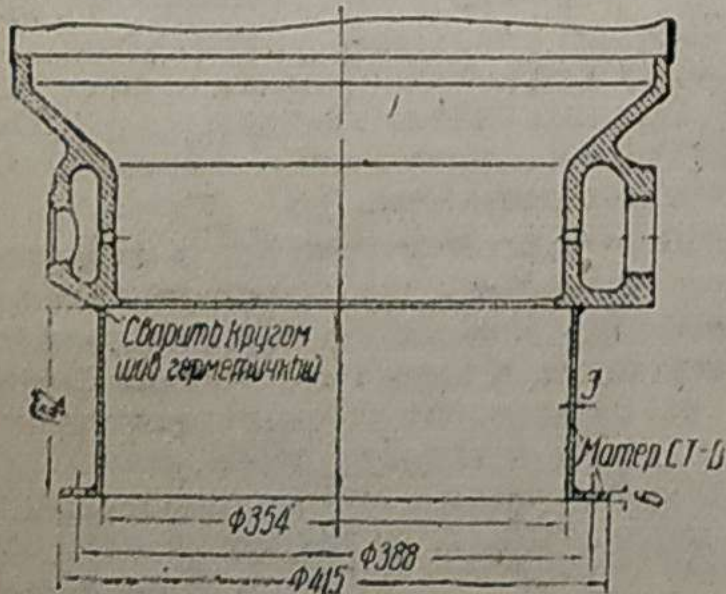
Приварка цилиндра для монтажа горловины ЗИС-21.
